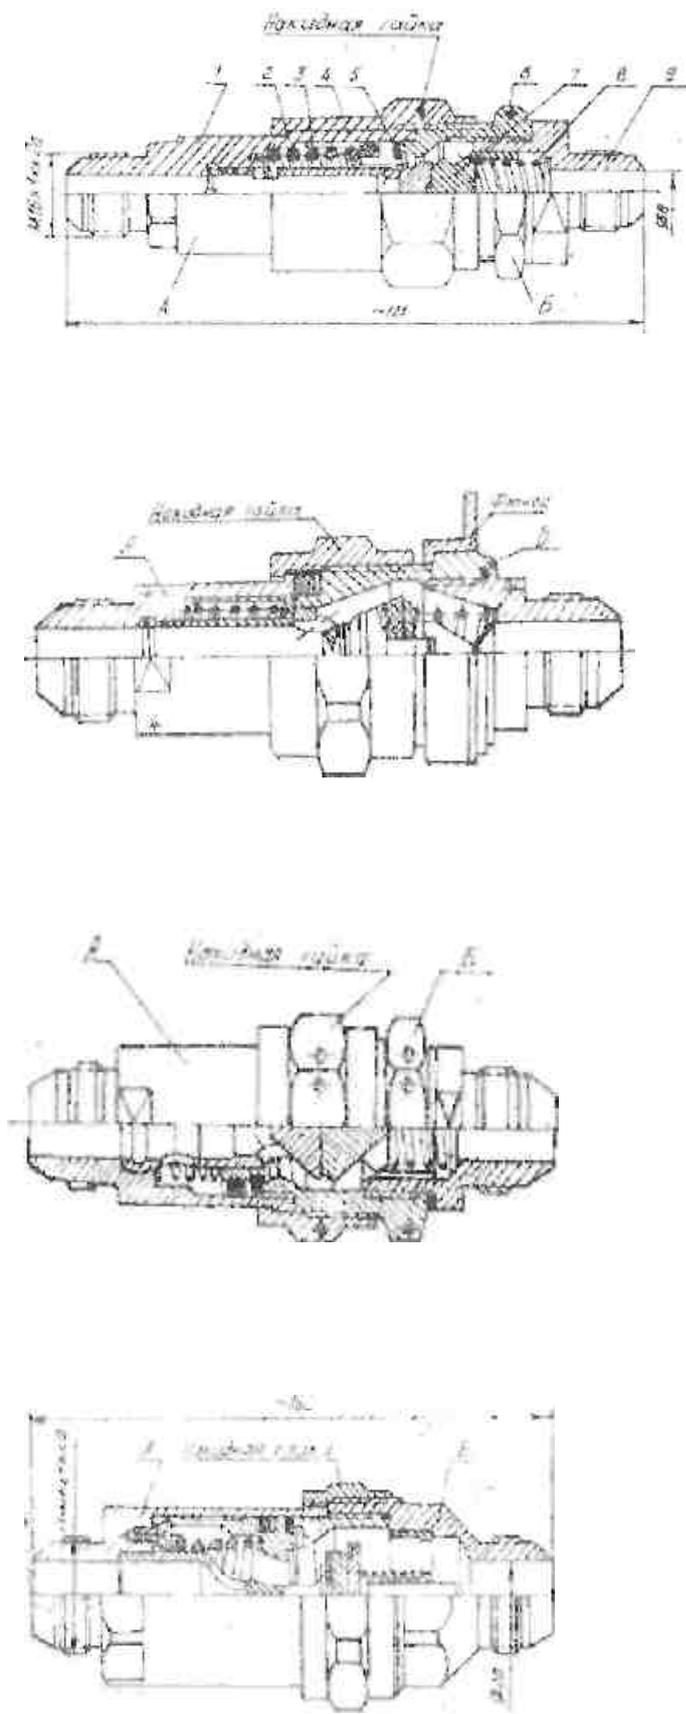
Клапаны разъемов с различными способами крепления грибка: а — крепление стопорным кольцом: 1 - корпус клапана А, 2- грибок, 3 — пружина, 4 — стакан (или втулка), 5 —уплотнительное кольцо, 6 — корпус клапана Б, 7 — клапан, 8 — пружина, 9 — штуцер; б, в —крепление развальцовкой; г —крепление винтами.
